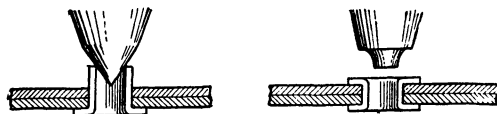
Заготовка отверстия под заклепку (а) и открытая клепка (б).
